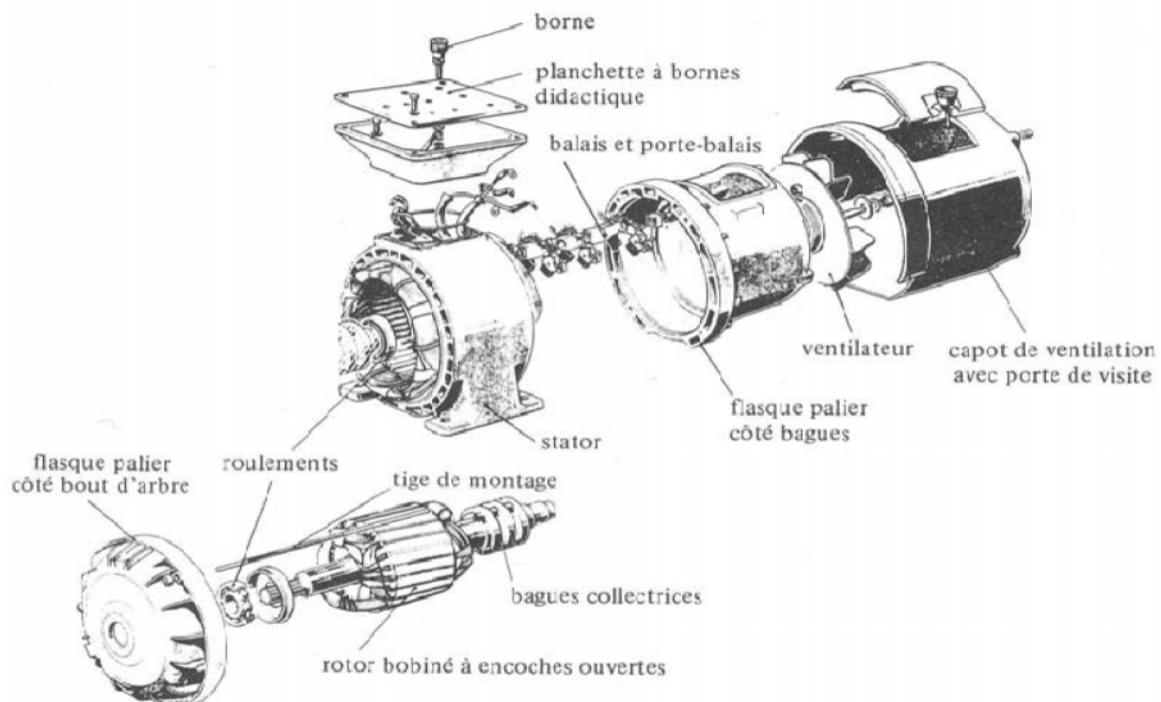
Vue éclatée d'une machine asynchrone triphasée à bagues.
